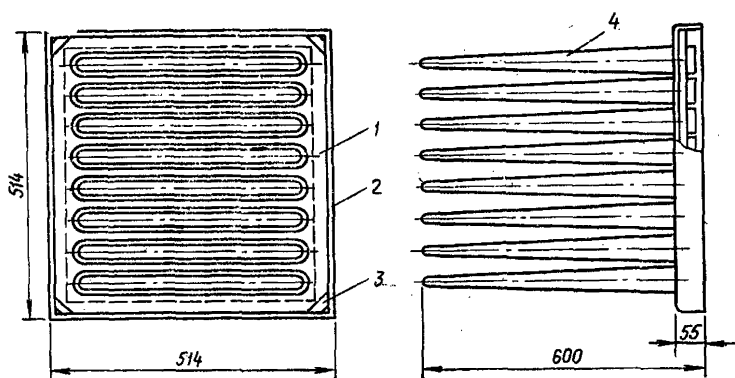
Габаритный чертеж карманного фильтра ФяКП
